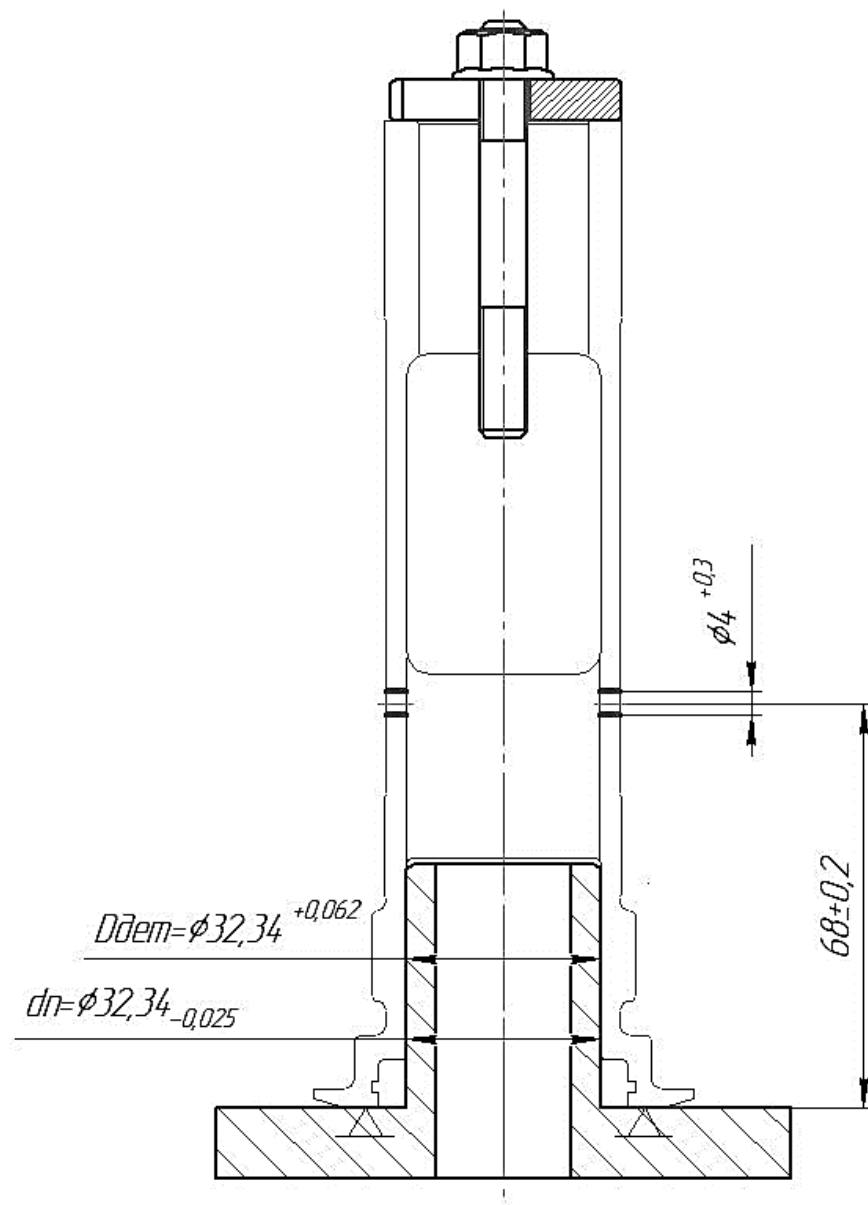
Схема встановлення деталі жорсткий циліндричний палець.
